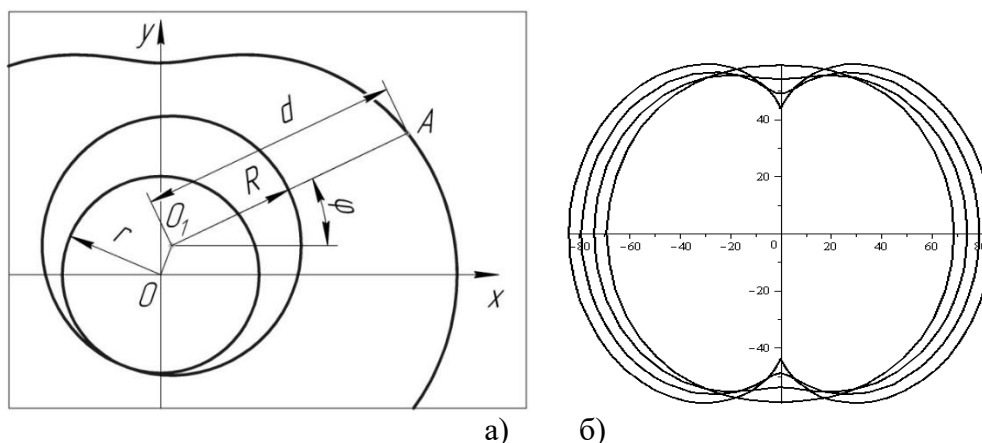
Формування профілю корпусу компресора: а – схема утворення
